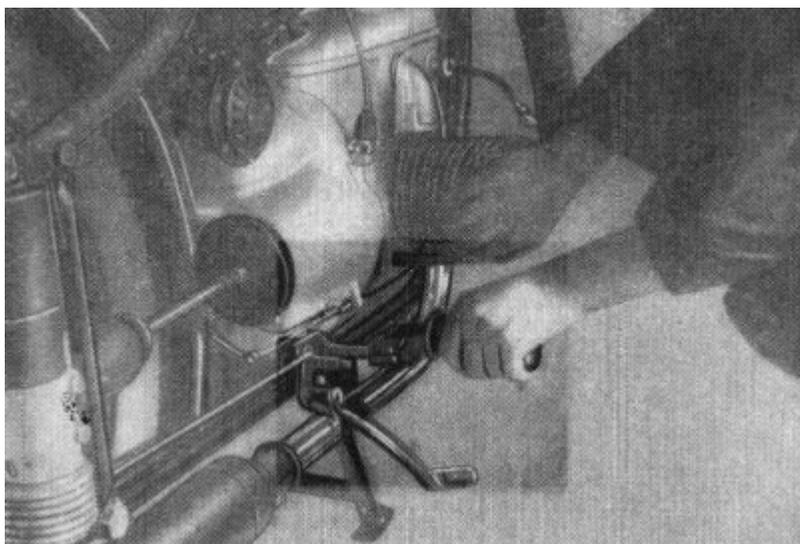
Motorausbau. Hinteren Befestigungsbolzen einschließl. rechter Fußraste herausziehen.
